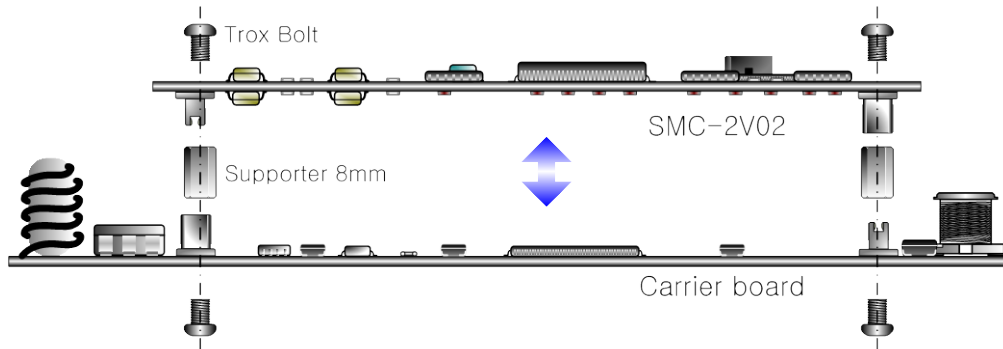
Carrier Board에 SMC-2V02를 고정하는 방법(그림 5 참조)
